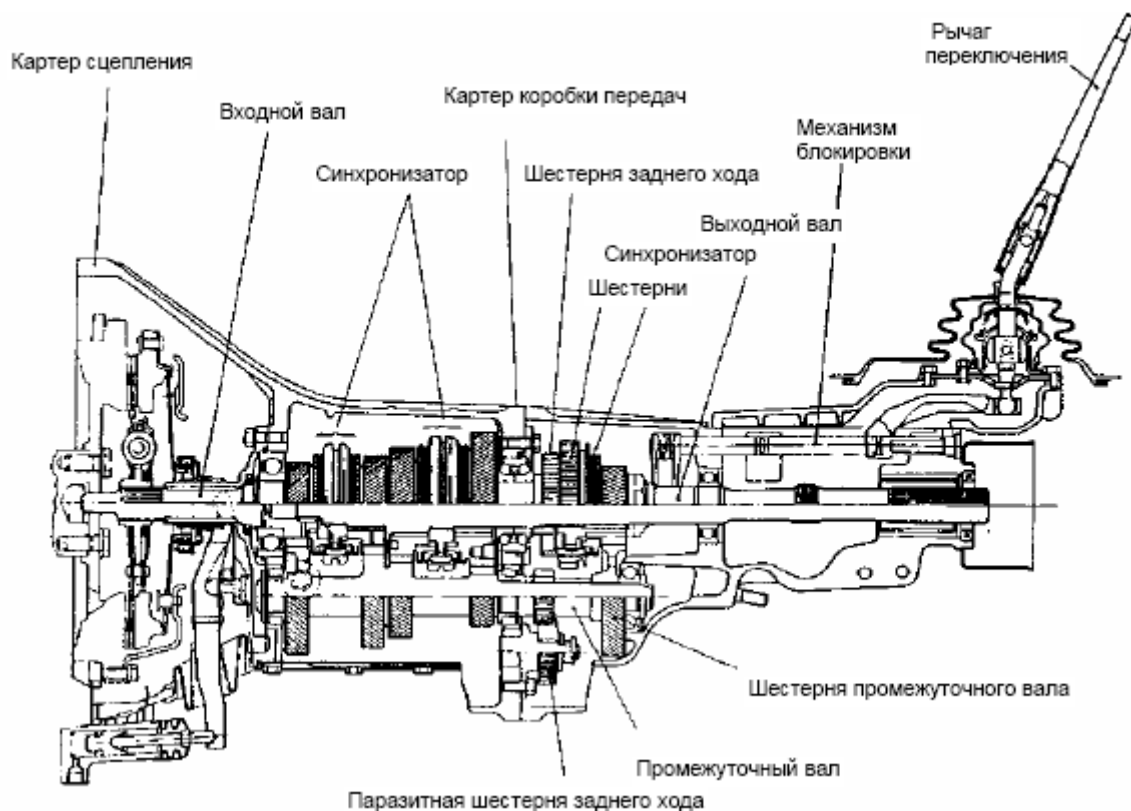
Устройство пятиступенчатой коробки передач заднеприводного автомобиля с передним расположением двигателя (FR)
